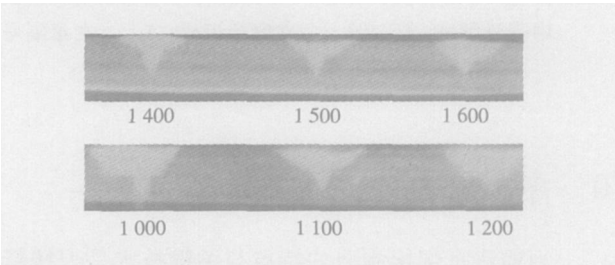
不同焊接速度 (mm/min) 下的焊缝截面
